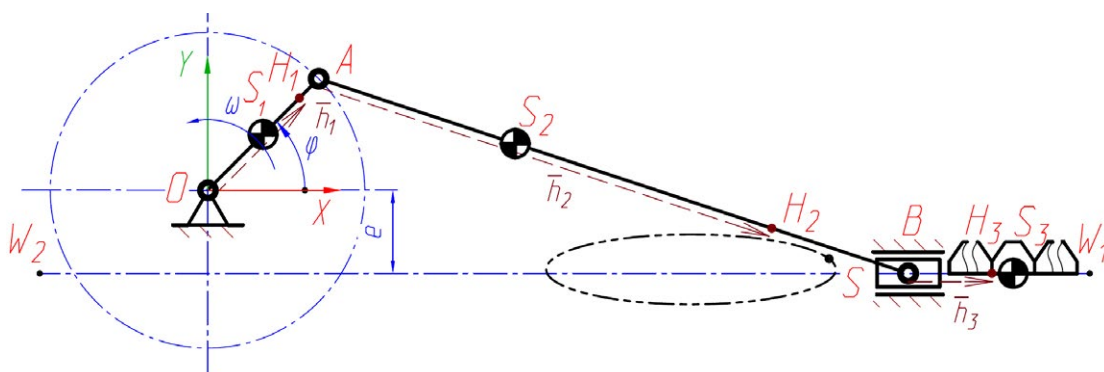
Кинематическая схема дезаксиального КПМ привода РА.
